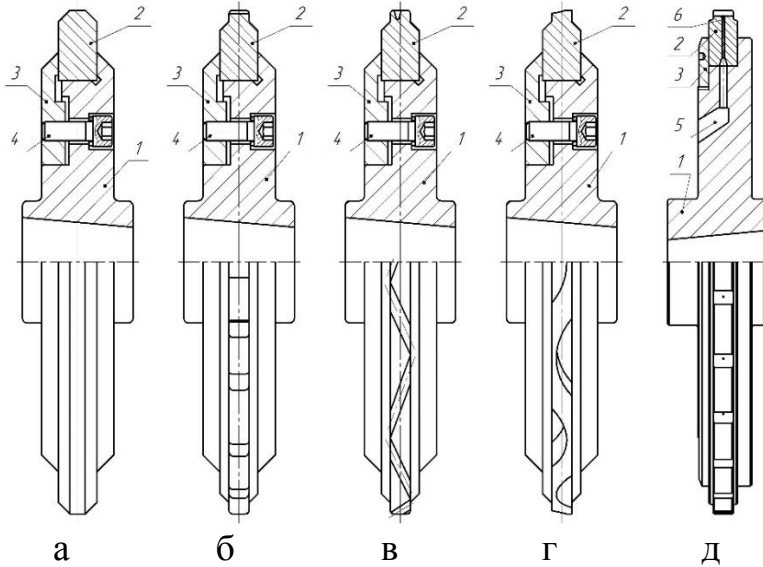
Інструменти для фрикційного оброблення з різною формою робочої поверхні: а) гладка; б) поперечні пазами; в) різнонаправлені пази; г – хвилеподібна; д) диск з внутрішньою подачею технологічного середовища: 1 – корпус, 2 – диск (з різною формою периферії); 3 – притискне кільце; 4 – болт; 5 – кільцева канавка для середовища; 6 – радіальний отвір
